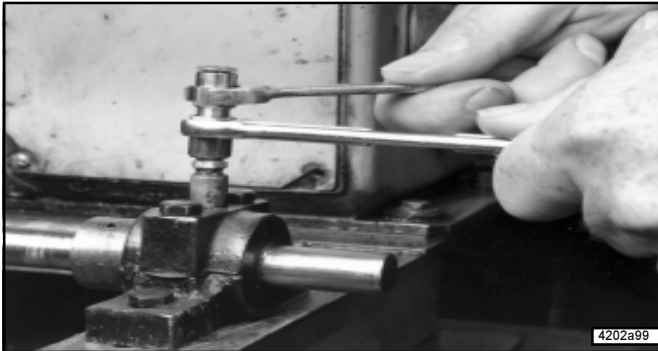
Quicklink Steckverschraubung in den Zerk-Lock-Körper einschrauben
